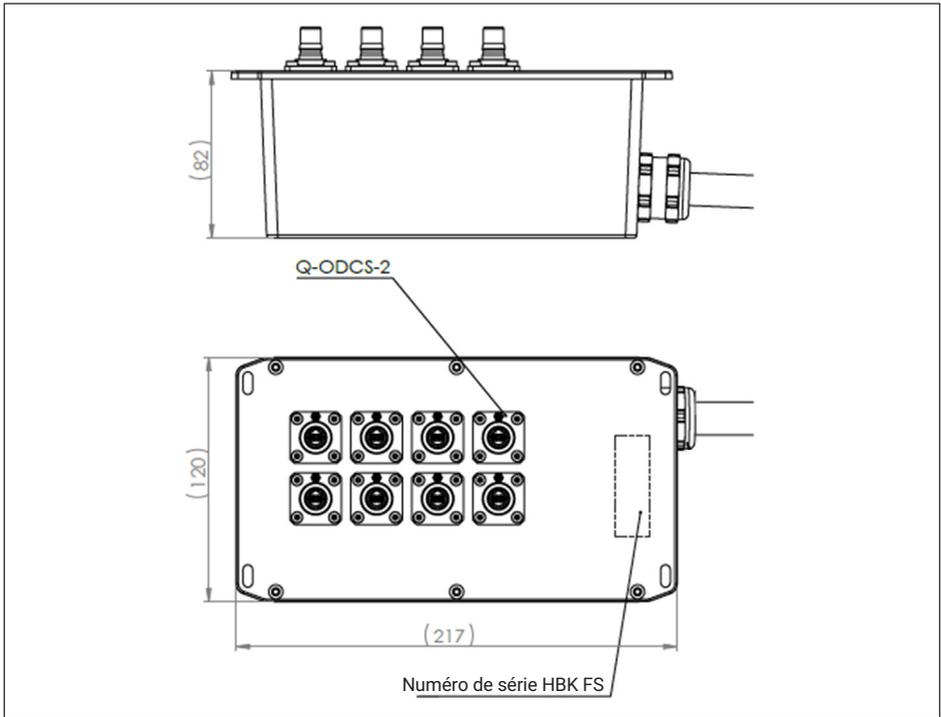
Boîtier d'interconnexion – Côté boîtier – Dessin technique (dimensions en mm)
